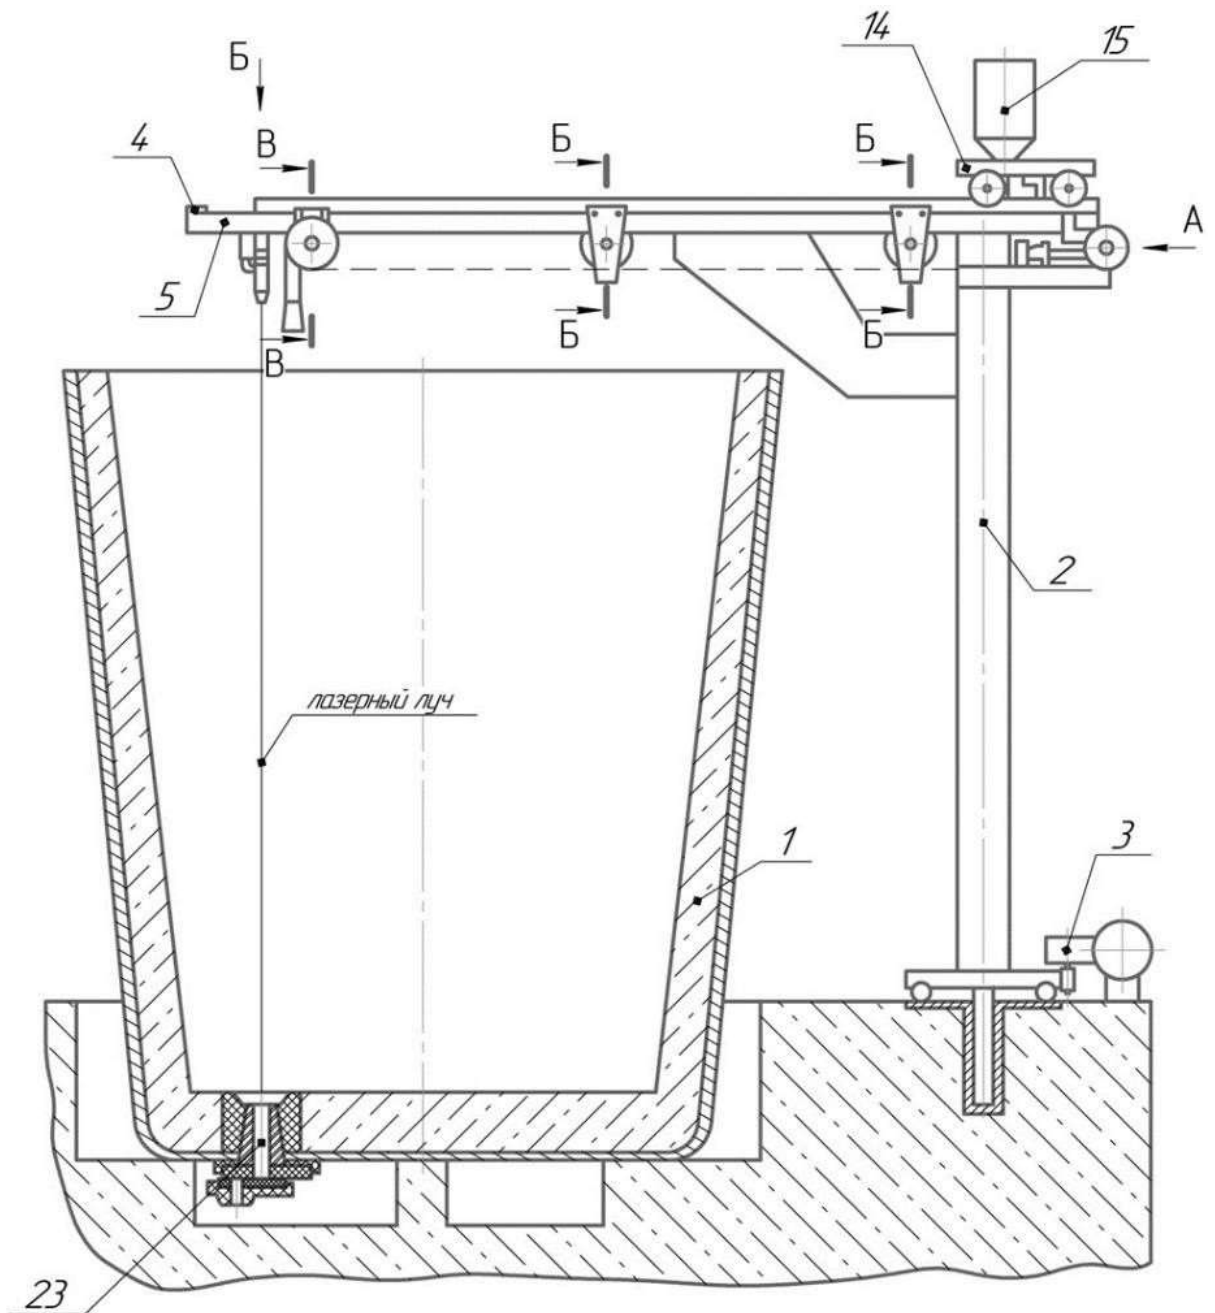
Конструктивная схема модернизированного манипулятора для механизированной подачи стартовой смеси в выпускной канал сталеразливочного ковша (начало).
